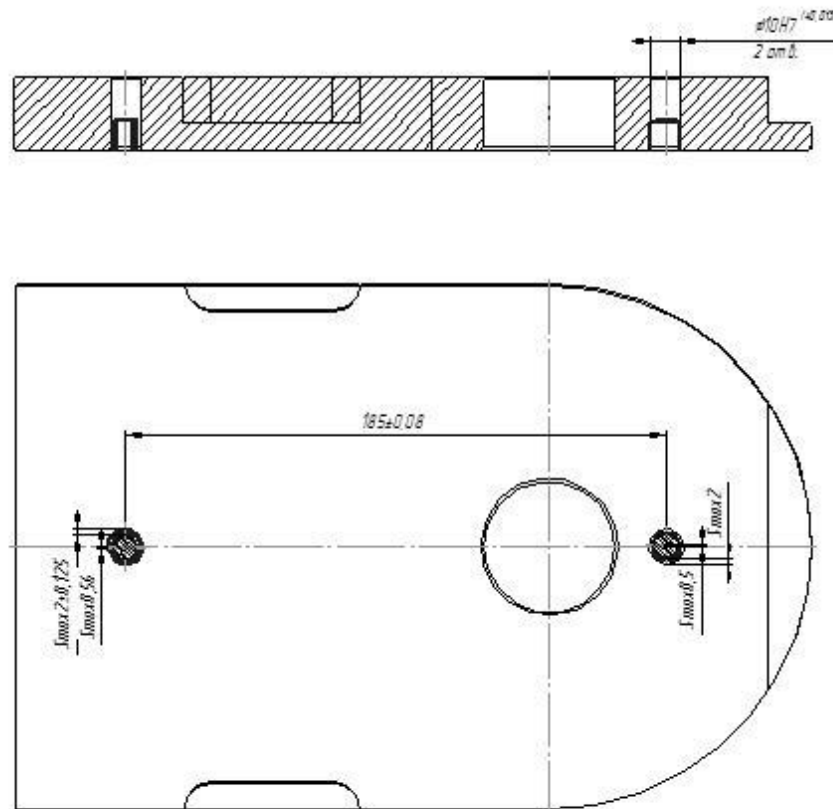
Схема установки детали "Плита" на цилиндрический и срезанный пальцы
